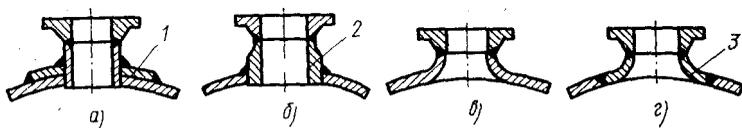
Способы соединения люков и штуцеров с корпусами аппаратов
